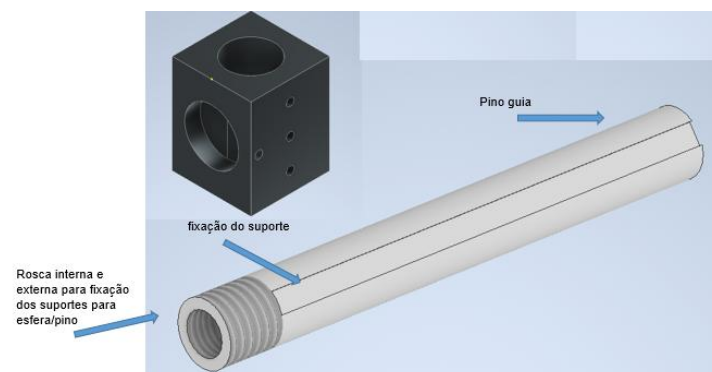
Componentes do conjunto de suporte do tubo cilíndrico
